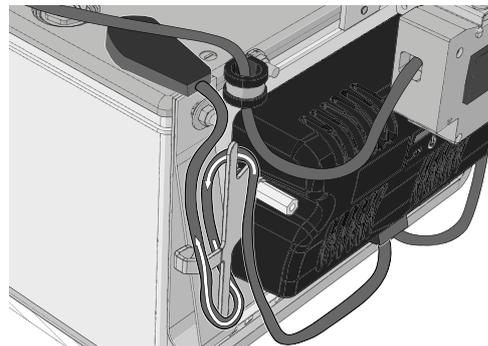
Conecte el cable que está conectado a la terminal trasera izquierda de la batería en su soporte de cable como se muestra.
